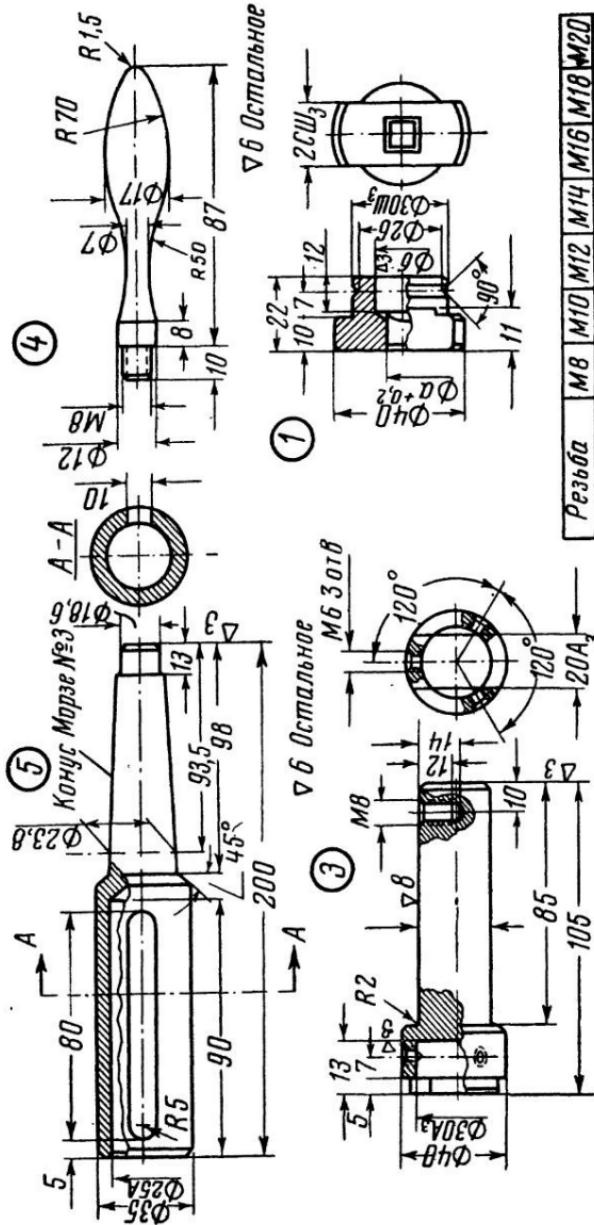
Детали приспособления для нарезания резьбы метчиками: I — держатель; 2 — корпус; 4 — ручка; 5 — ползун;
